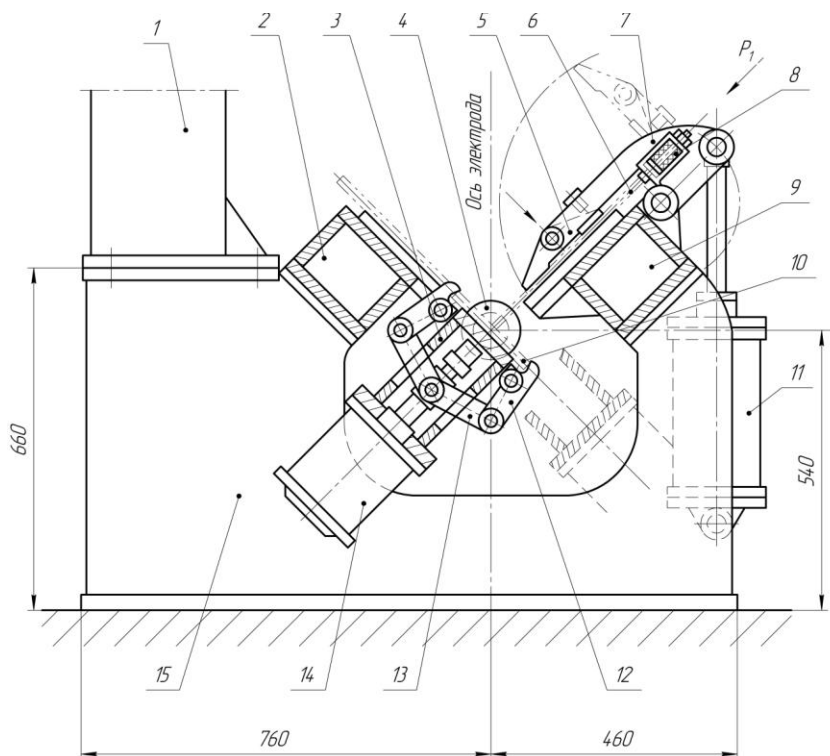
Кондуктор – кантователь для сборки и сварки тавровых балок
